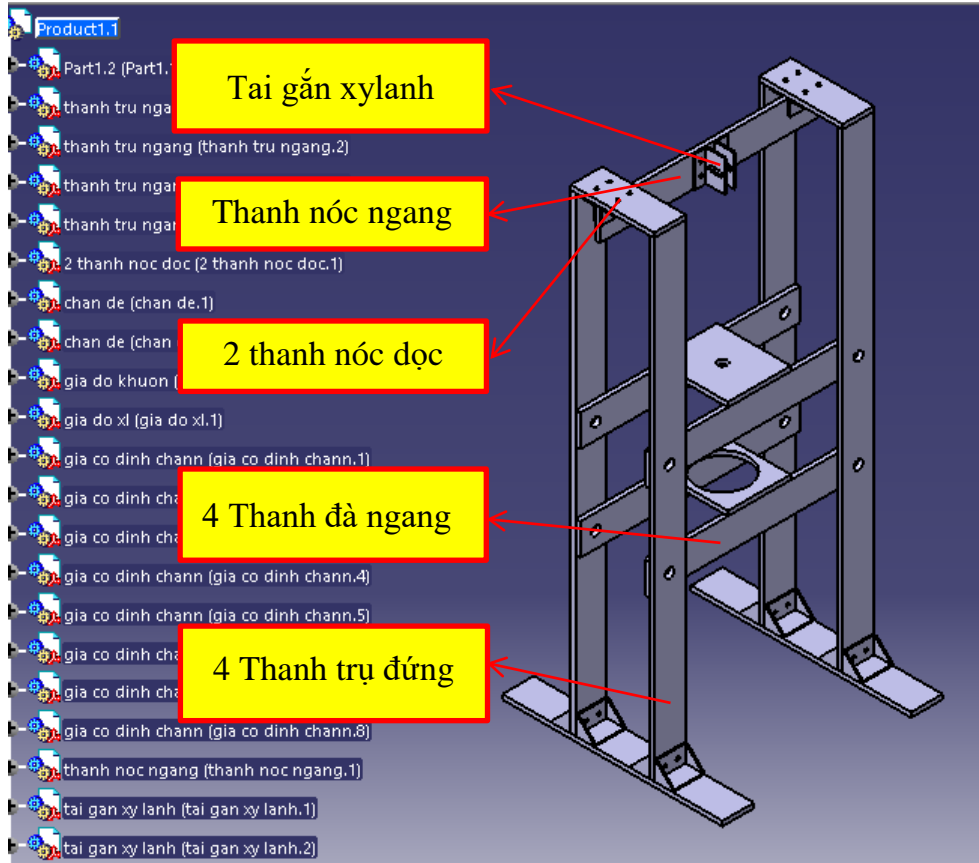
Mô hình tổng thể máy ép rác kiểu piston
